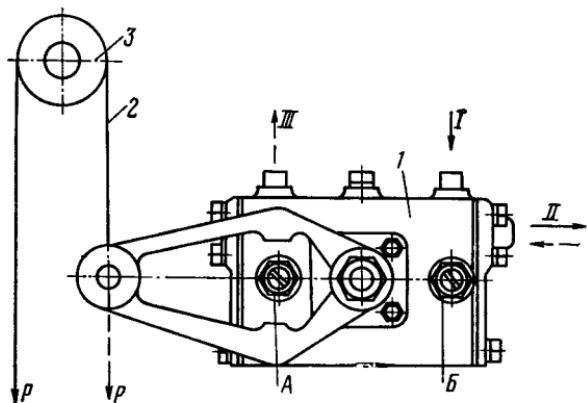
Схема стенда для регулировки времени замедления регулятора положения кузова
